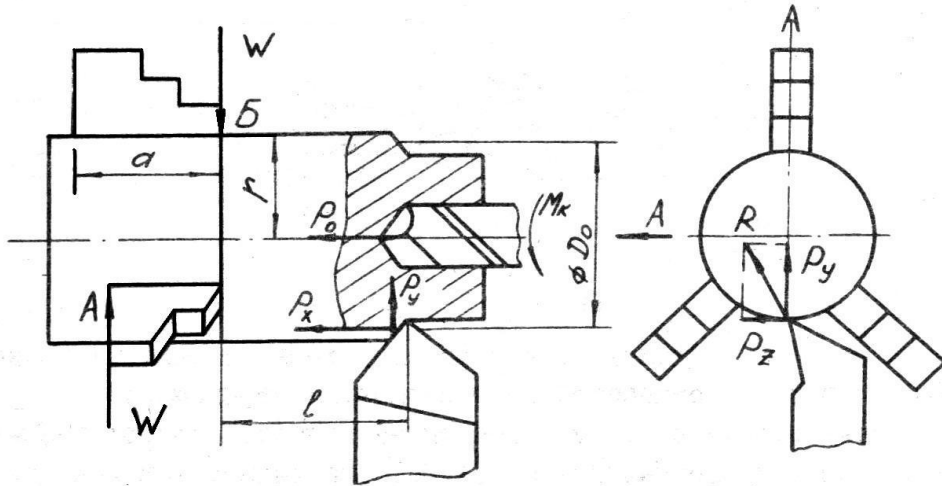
Схема установки і визначення зусилля затиску при одночасному свердленні отвору і обточуванні зовнішньої поверхні заготовки, яка закріплена в трьохкулачковому патроні
